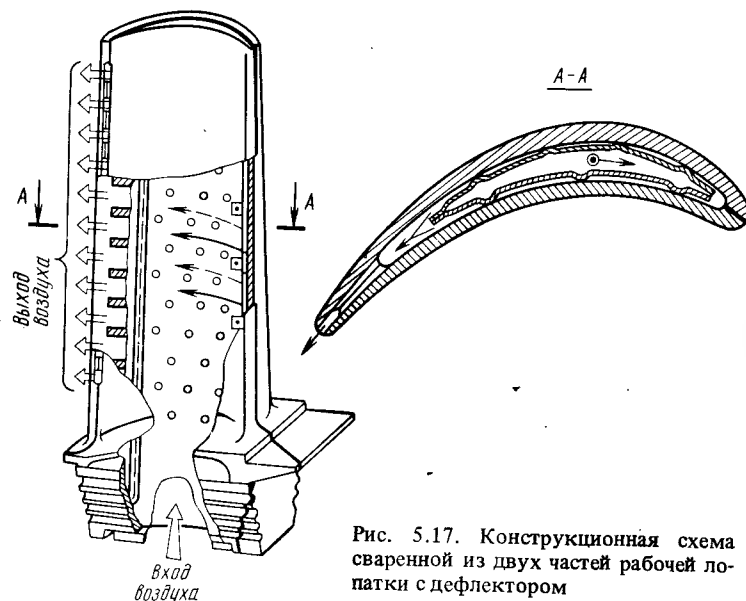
Конструкционная схема сваренной из двух частей рабочей лопатки с дефлектором
